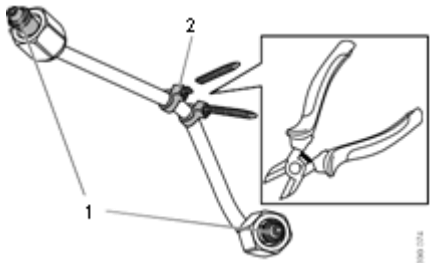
43 tubo de alta presión. fuente: multiweb taller Scania Concepción.
